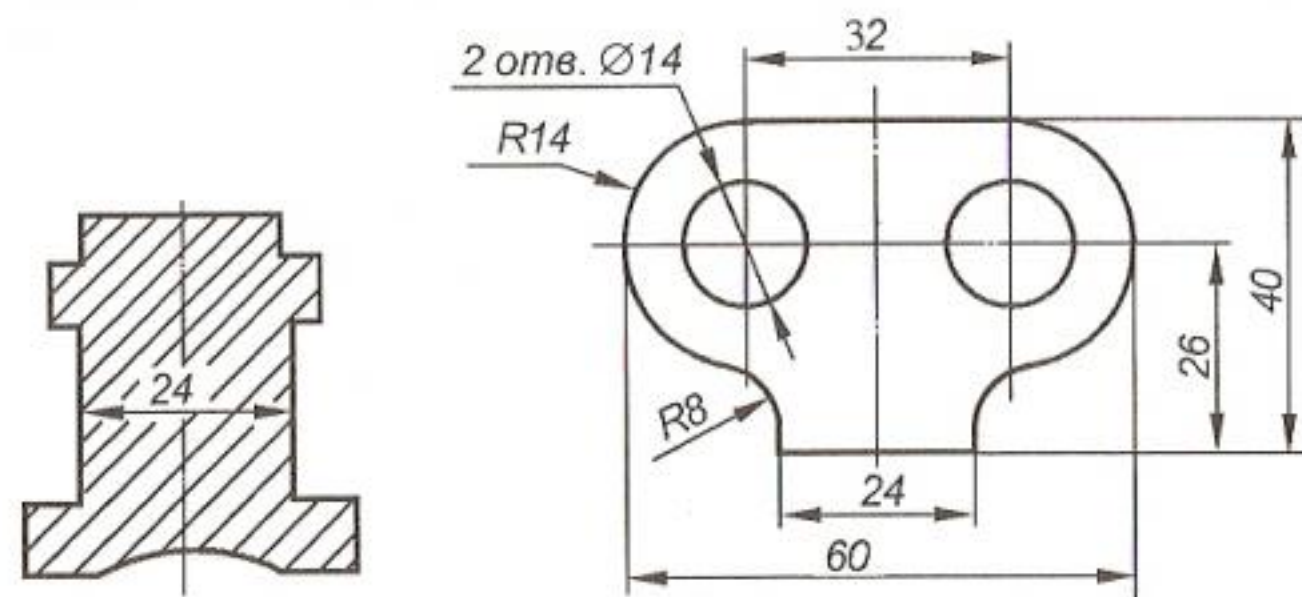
Прерывание осевой линии и линий штриховки в месте нанесения размерного числа
